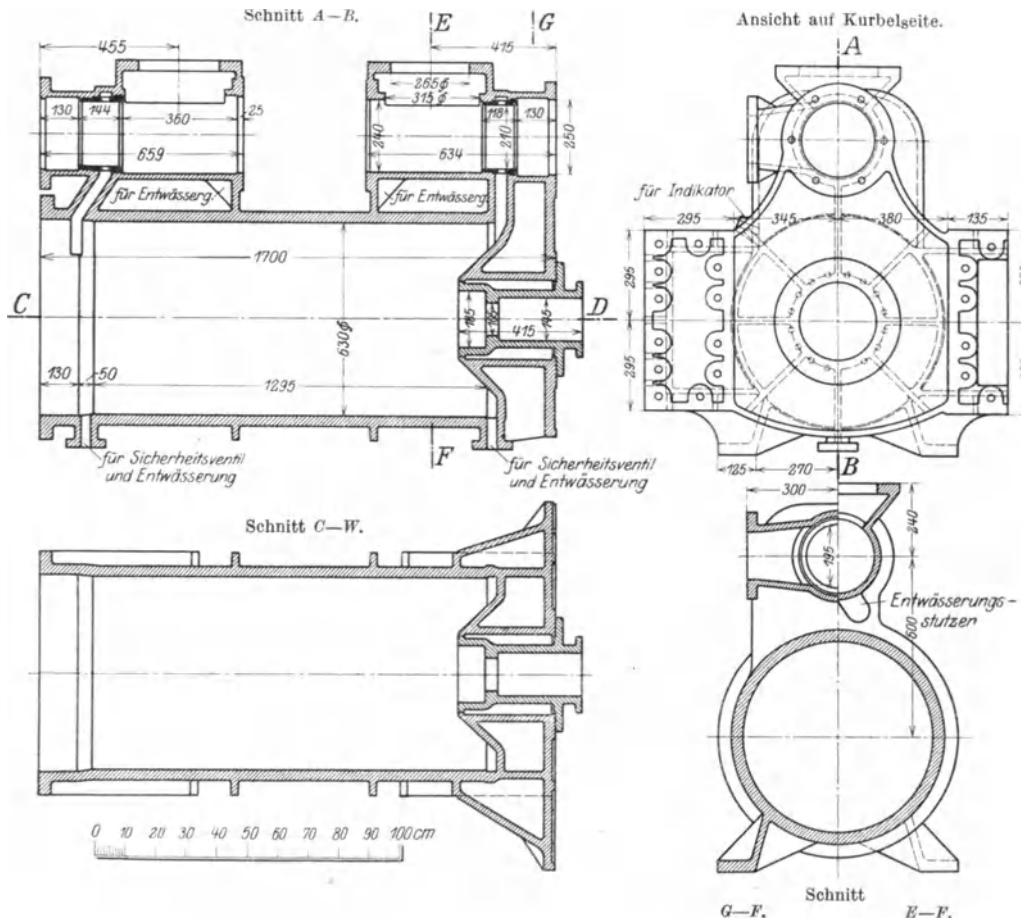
H. D.-Zylinder einer Radschiffsmaschine.
